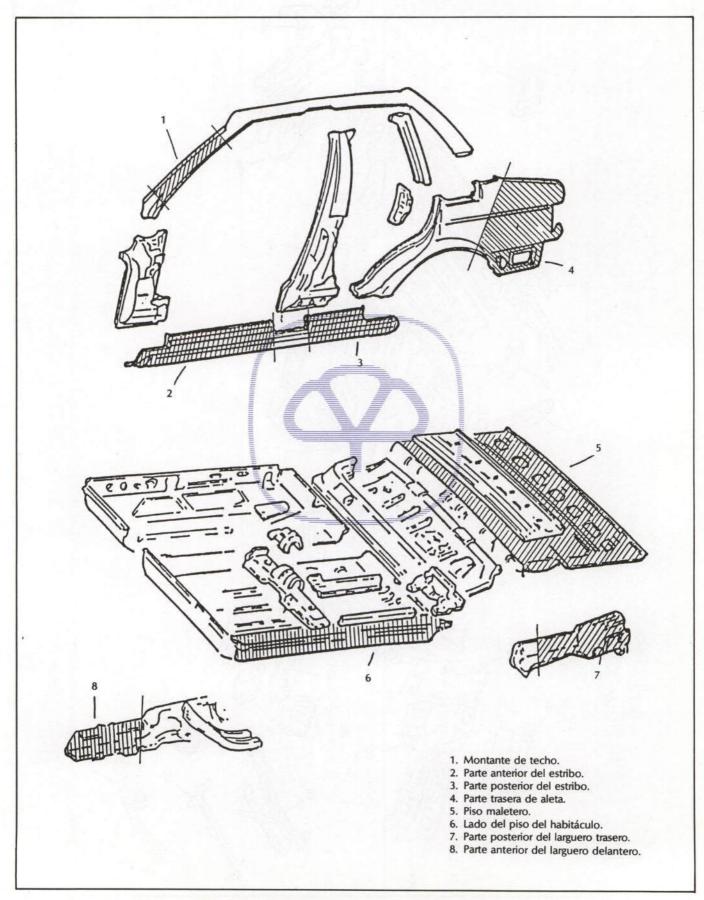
Secciones de ahorro que contempla el fabricante.
